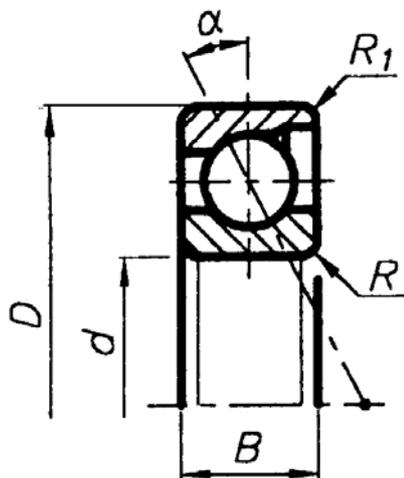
Габаритные размеры шариковых радиально-упорных подшипников
